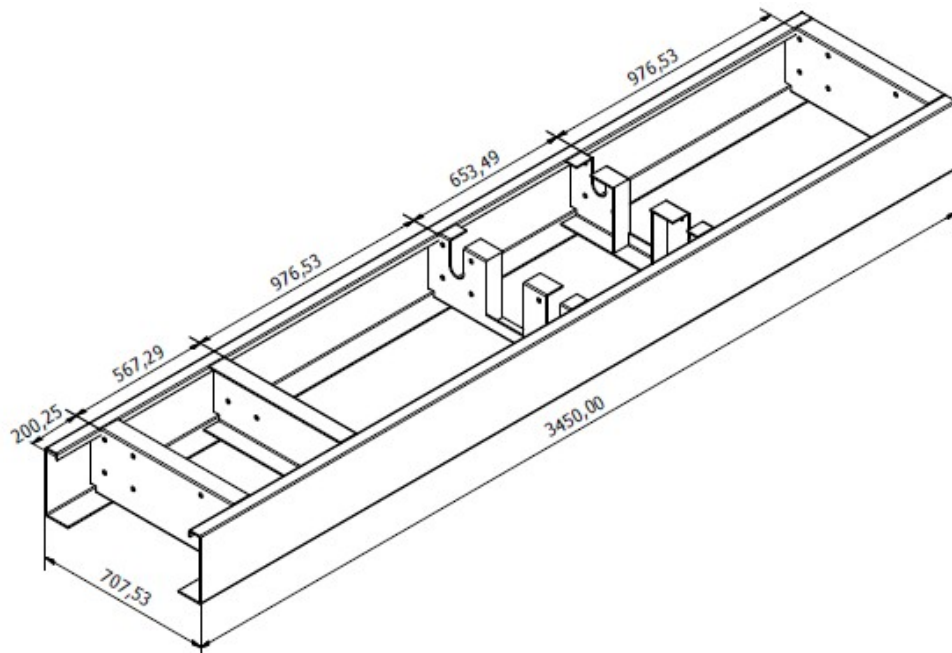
Vista de conjunto del chasis del dinamómetro ensamblado
